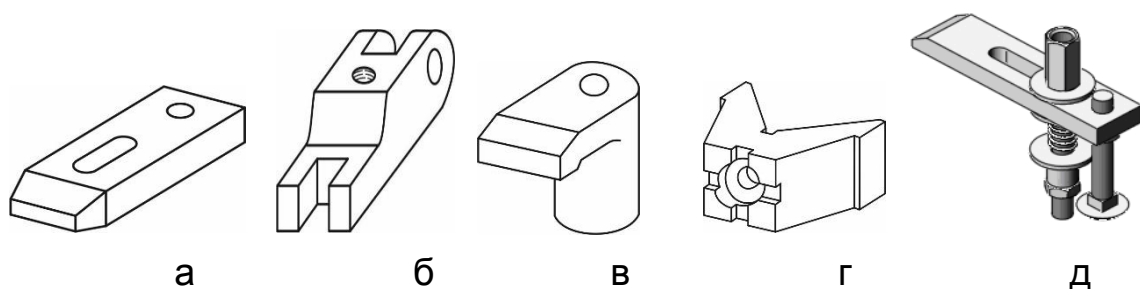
Примеры прижимных деталей и устройств: а – планка передвижная плоская; б – планка поворотная; в – наконечник Г-образный; г – наконечник призматический; д – прихват
